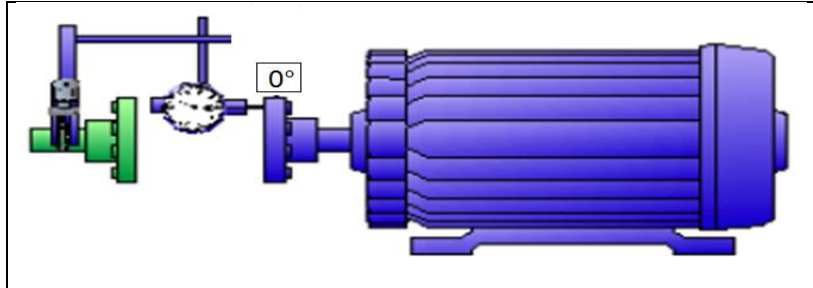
Posición inicial de medición FACE. Vista lateral de motor.
